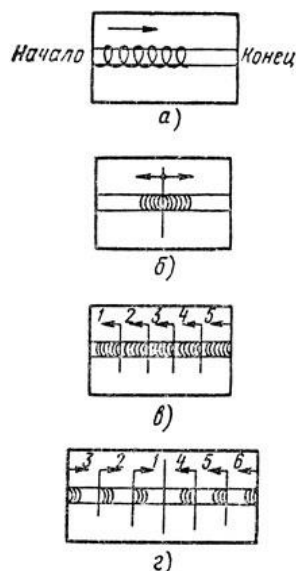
Схема сварки швов различной протяженности: а - сварка на проход для выполнения коротких соединений; б - сварка соединений средней длины от середины к концам шва; в - сварка обратноступенчатым способом для выполнения соединений средней длины (1 - 5 - последовательность наложения швов); г - сварка обратноступенчатым способом от середины к концам шва для выполнения длинных соединений
